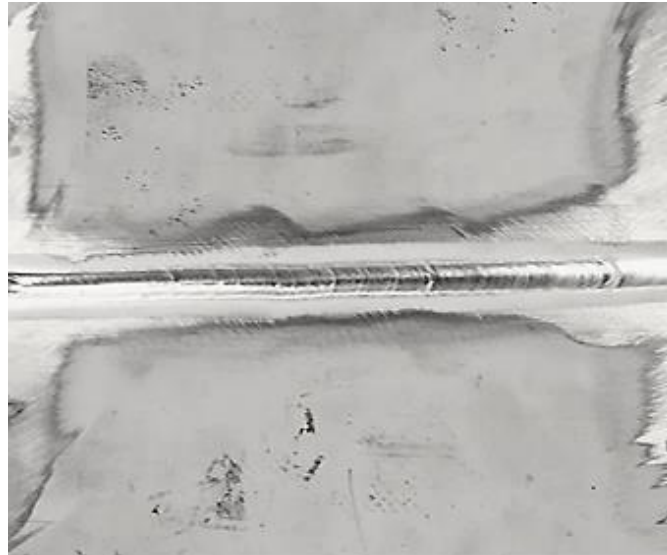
Cupón soldado en óptimas condiciones sin material de aporte
